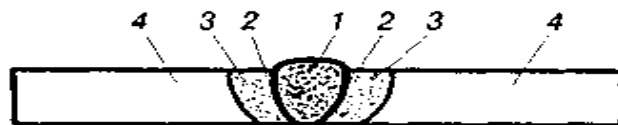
Будова зварного з'єднання: 1 – метал шва; 2 – зона сплавлення; 3 – зона термічного впливу; 4 – основний метал
